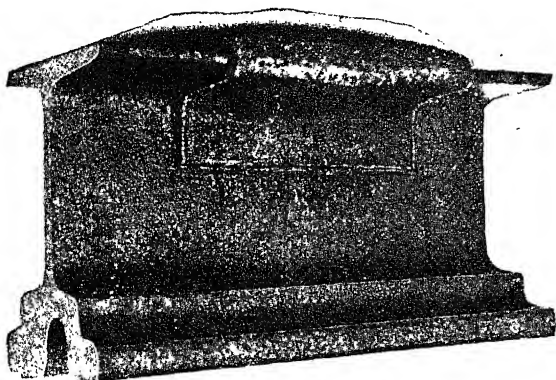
Éclissage de patin de rail en fer soudé par l'aluminothermie.
